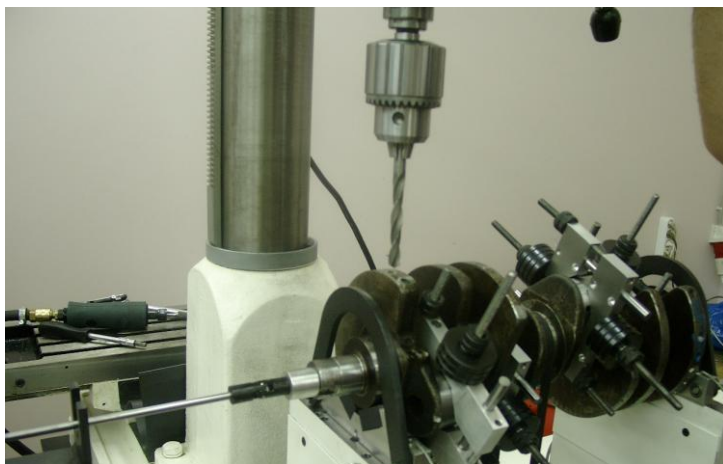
Окончательная балансировка коленчатого вала с учетом развесовки поршней и шатунов
